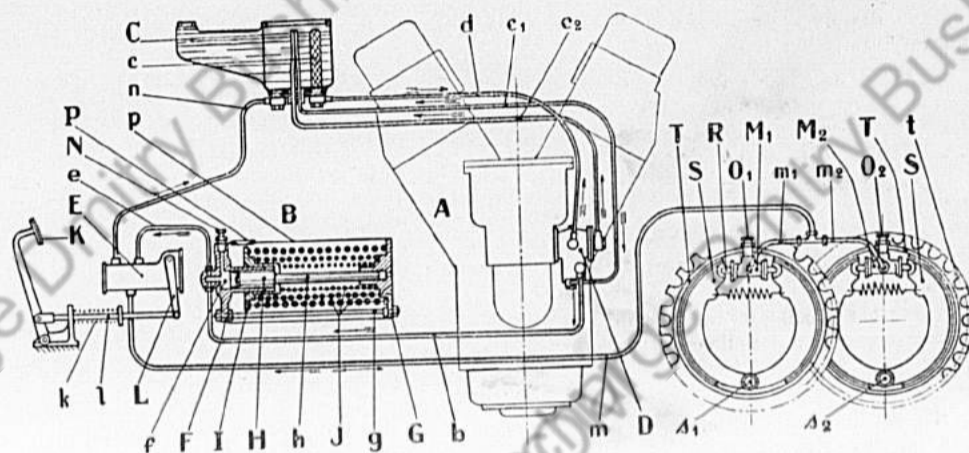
Fußbremse, auf die Triebräder der Gleisketten wirkend.
